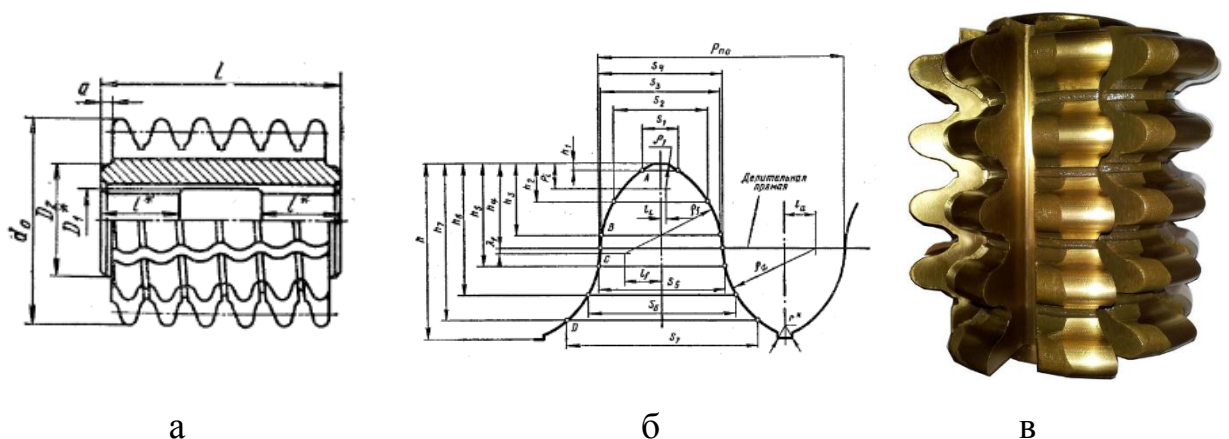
Черв'ячна фреза для нарізування евольвентних зубчастих коліс:
